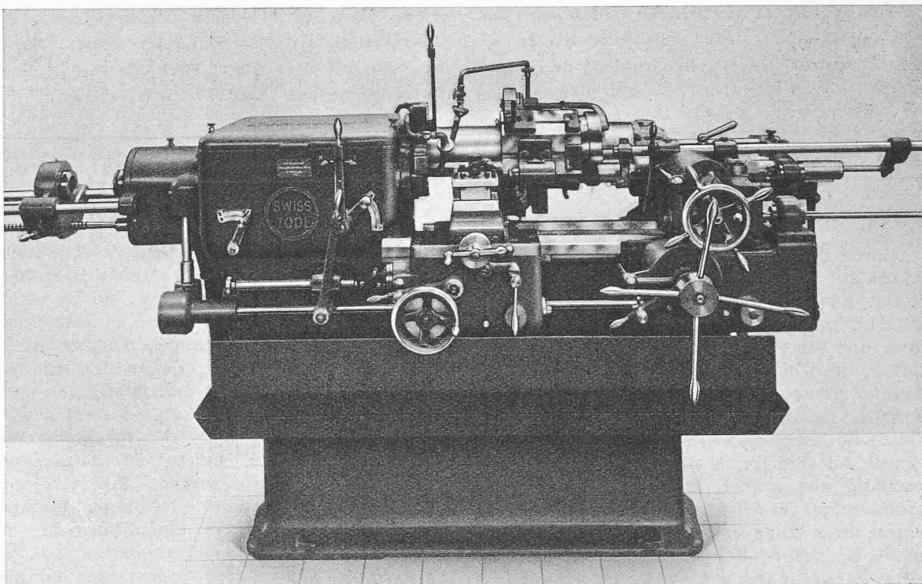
«Original Schaerer» Stangen-Revolverdrehbank. Schweiz. Werkzeugmaschinen A. G. Zürich
